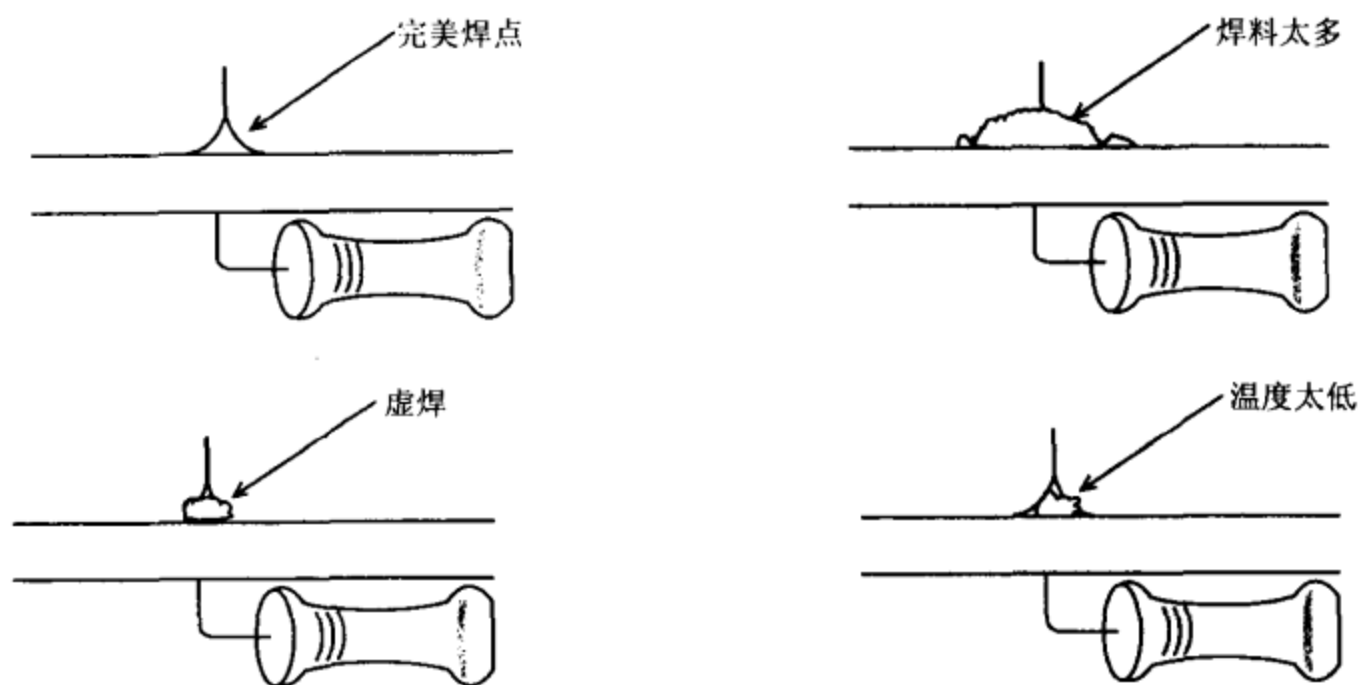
完美的焊接点和一些有问题的焊点
